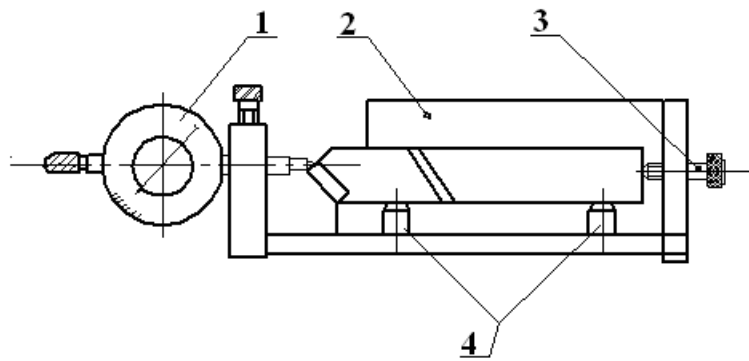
Схема лабораторної установки для визначення розмірного зношування лезового інструменту.
